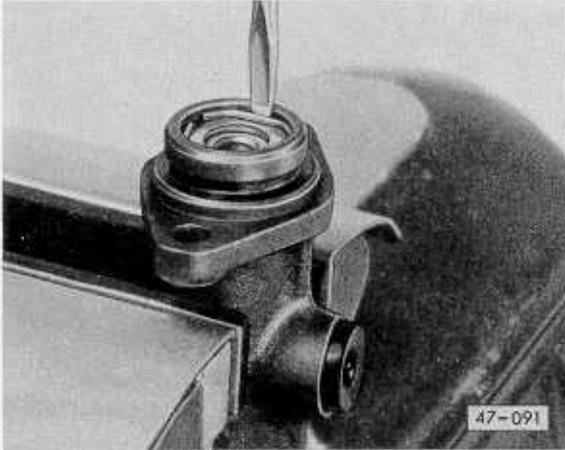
Sicherungsring mit Schraubenzieher heraushebeln.
